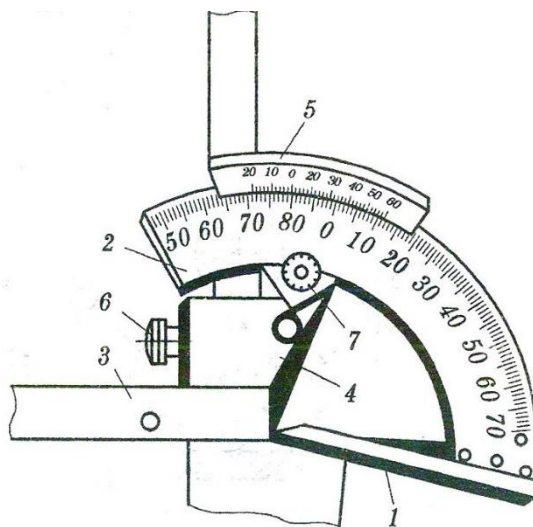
Угломер конструкции Семенова: 1 - линейка, 2 - дуга; 3 - угольник; 4 - державка; 5 - сектор; 6 и 7 – винты
